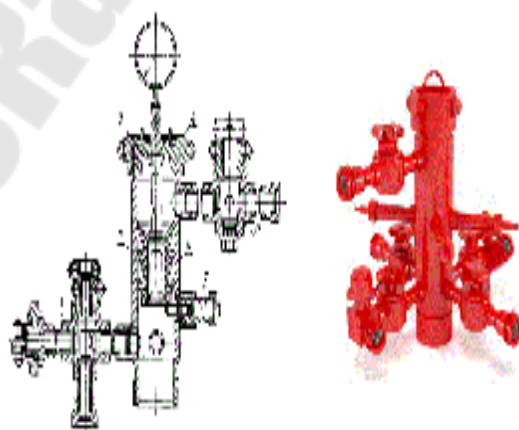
Головка цементировочная универсальная ГЦУ: 1 – обвязка; 2 – корпус; 3 – крышка; 4 – накидная гайка; 5 – пробковый кран; 6 – цементная пробка; 7 – стопорный винт
